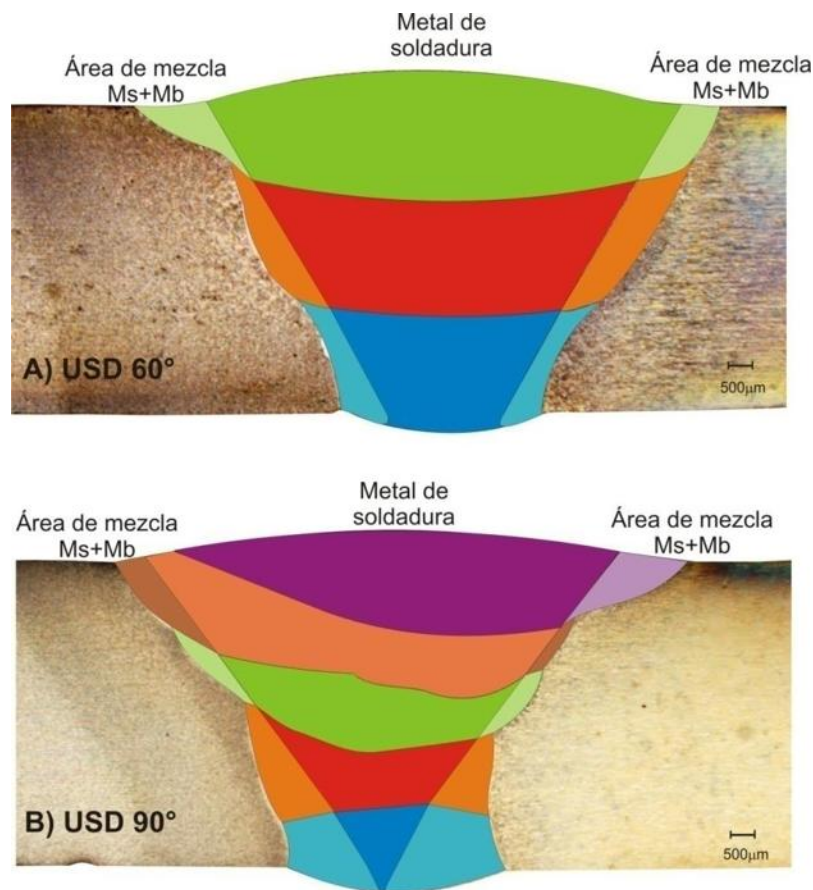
Dilución del metal de soldadura en las uniones soldadas disímiles
